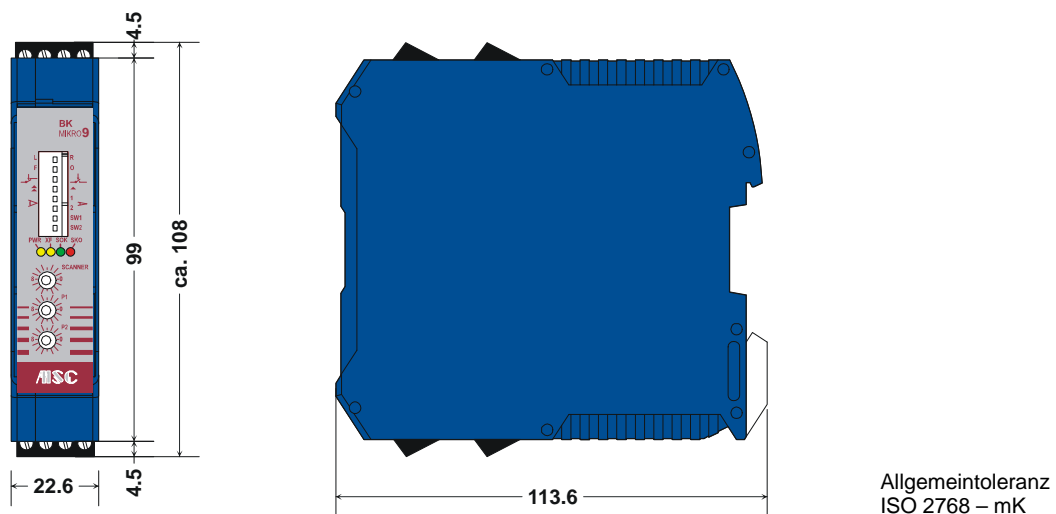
Mechanische Abmessungen – I/O Erweiterungsmodul
